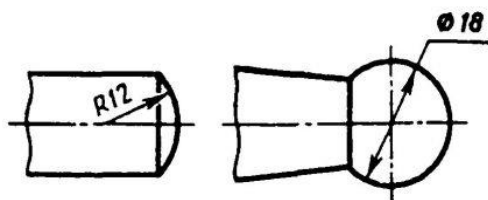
Образец нанесения диаметра и радиуса конструкции
